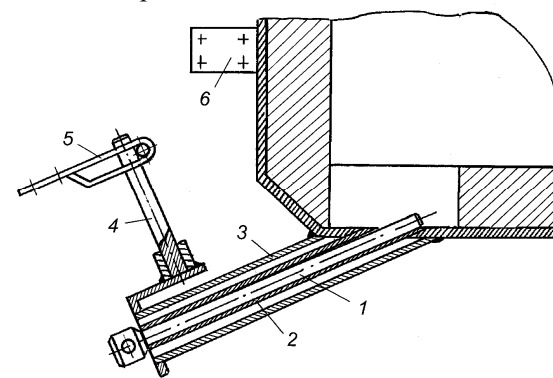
Устройство для слива металла Доре: 1 – конус; 2 – труба сливная; 3 – труба обогревающая; 4 – штанга токоподводящая; 5 – шина; 6 – контакт на корпусе испарителя.
